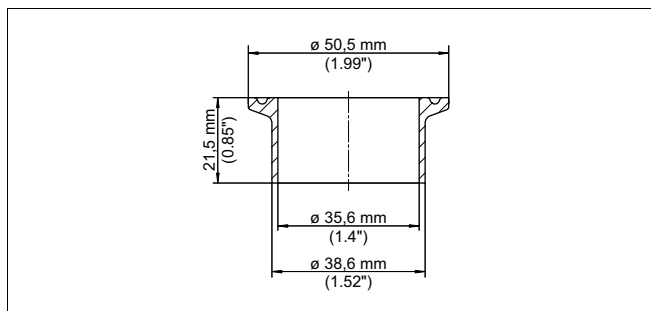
Medidas da luva soldada Clamp 1½" PN16 DIN 32676, ISO 2852/316L
